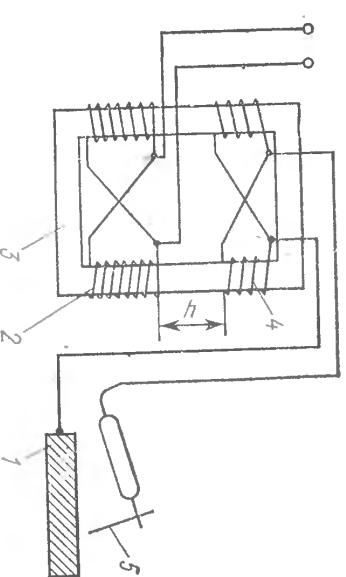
Электрическая схема сварочного трансформатора с перемещением вторичной обмотки:
